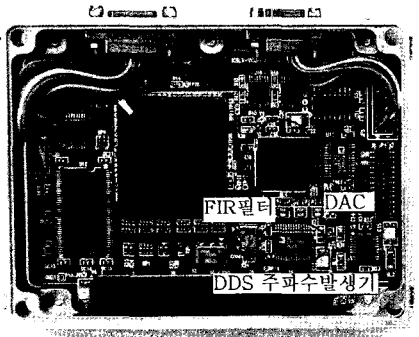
구현된 RF 인터페이스 PCB 보드 1
